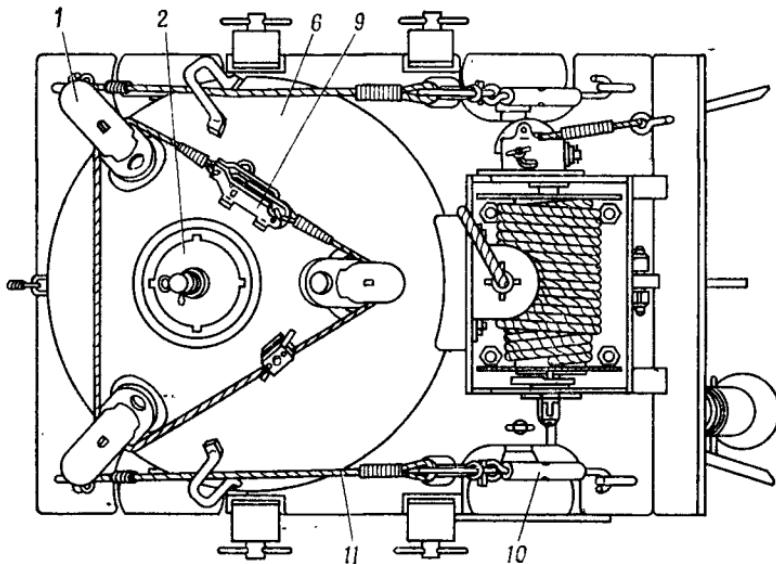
Мина ПДМ-ЗЯ (вид сверху):
